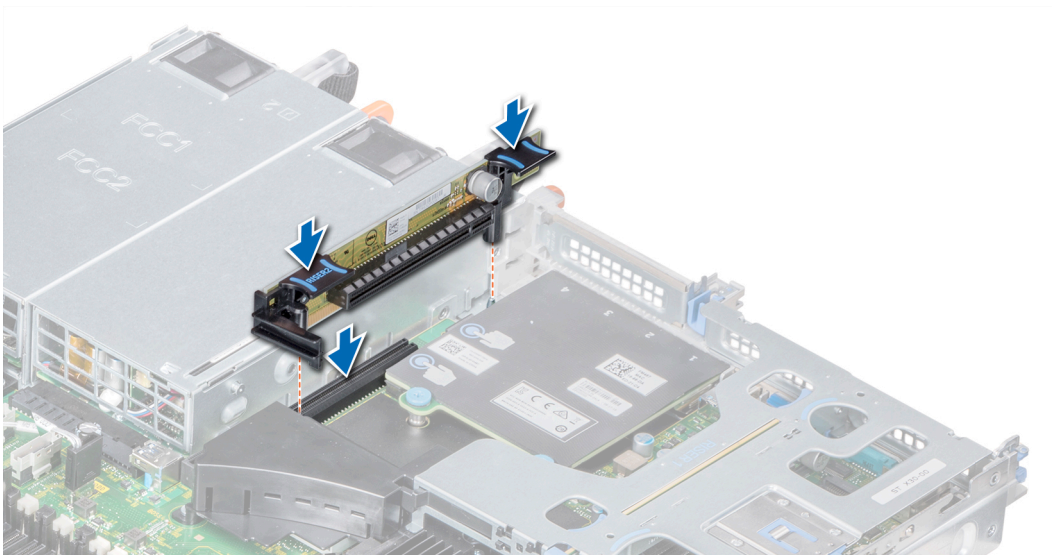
Installation de la carte de montage pour cartes d'extension 2A
